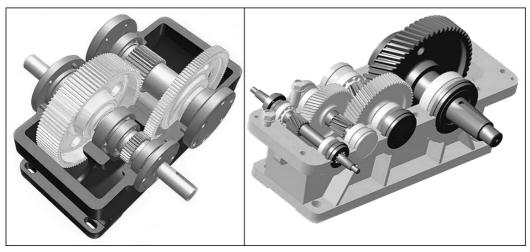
Примеры редукторов с прямозубыми и косозубыми зубчатыми колесами
